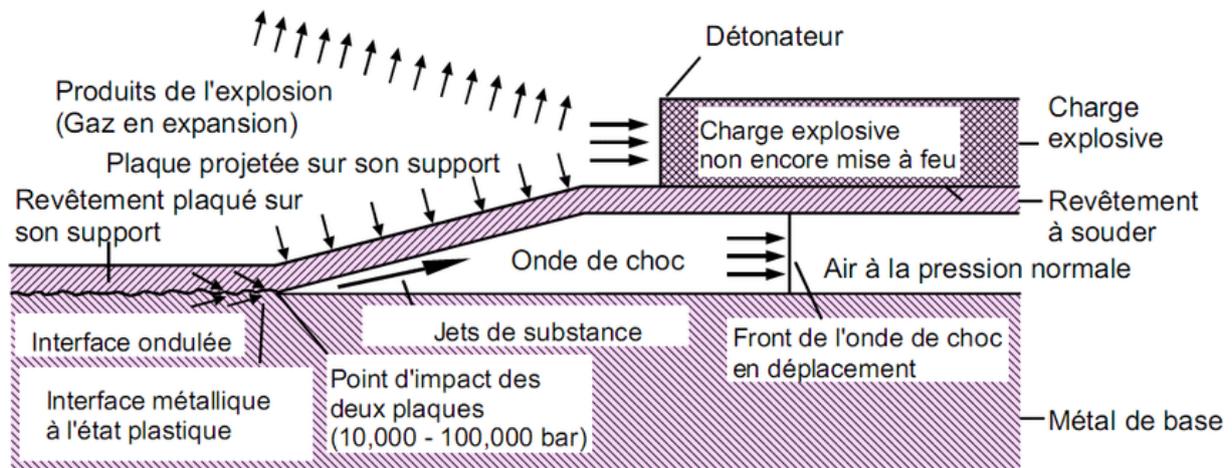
Schéma de principe du soudage par explosion.
